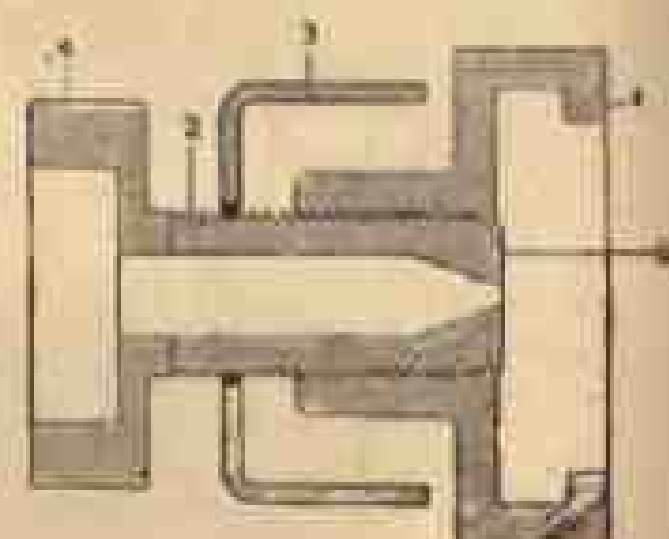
Разрез съёмника втулки винта новой конструкции.
